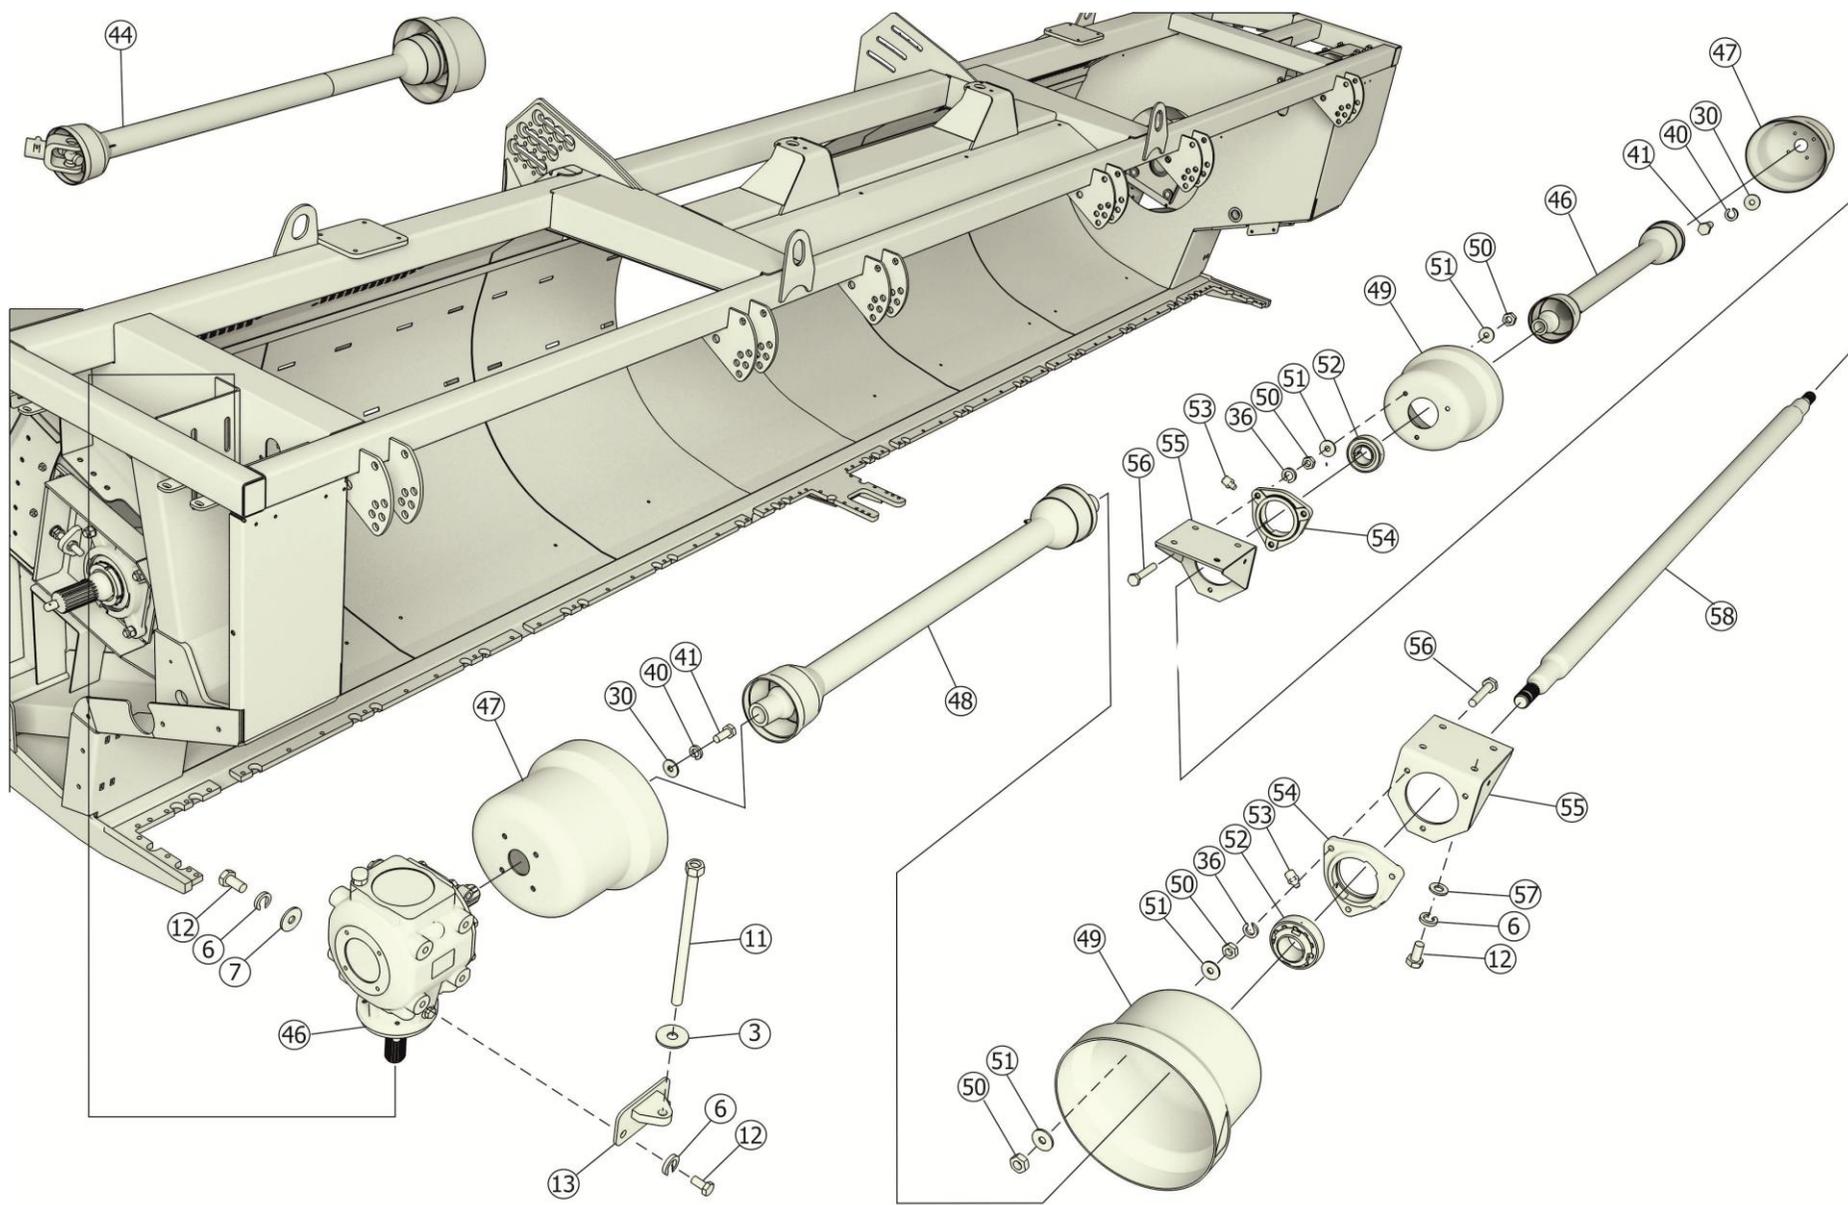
Установка приводов ЖРН-604.06.00.000А
